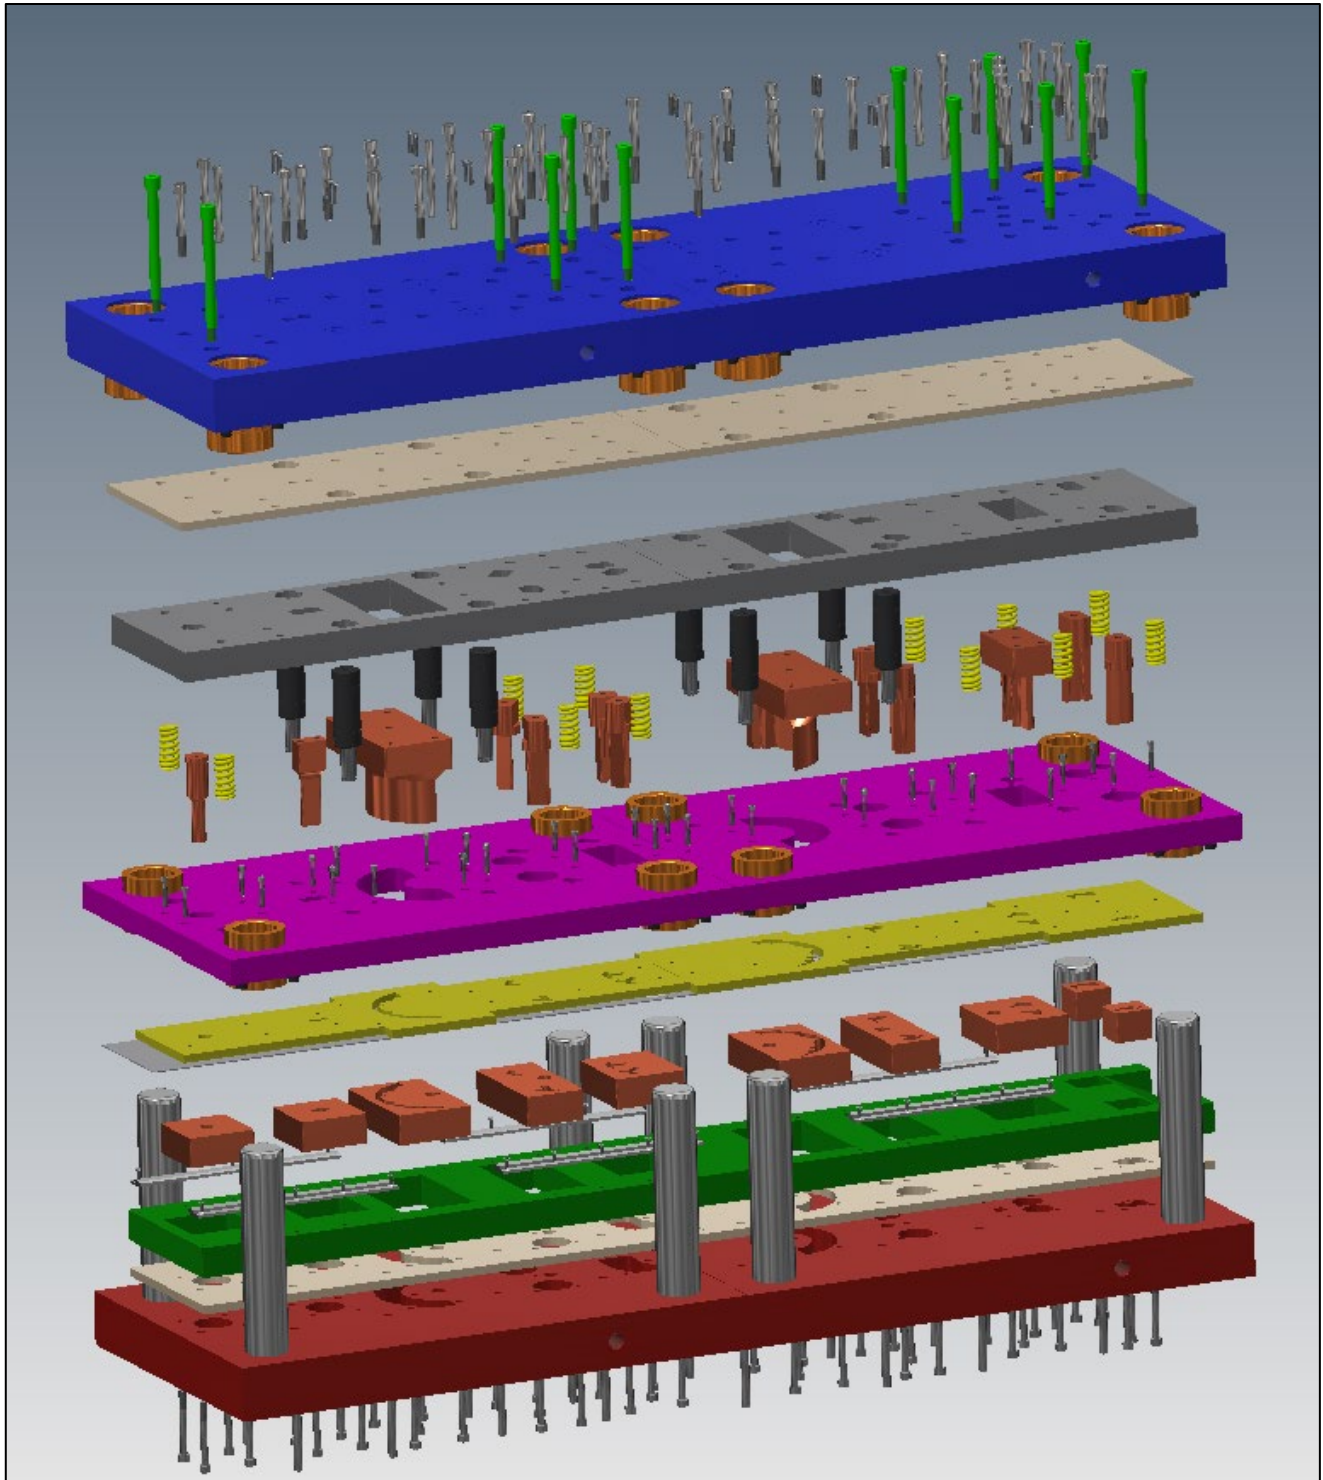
Vista en explosión del troquel con elementos comerciales.
